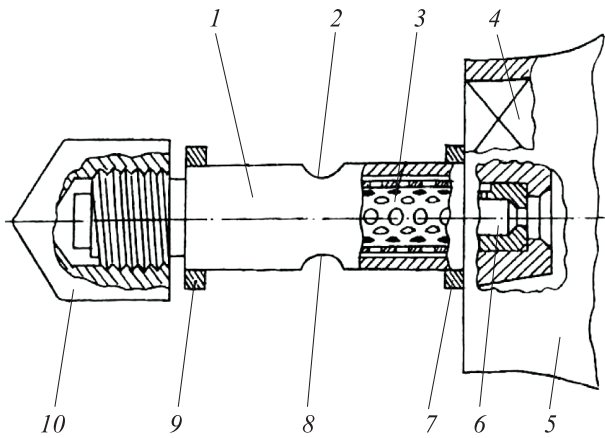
Конструктивная схема штатной ОТФ воздушно-реактивного двигателя семейства НК: 1 — корпус; 2, 8 — входные отверстия; 3 — сетчатый фильтр; 4 — завихритель; 5 — отражатель; 6 — распылитель; 7, 9 — выступы для крепления; 10 — гайка
